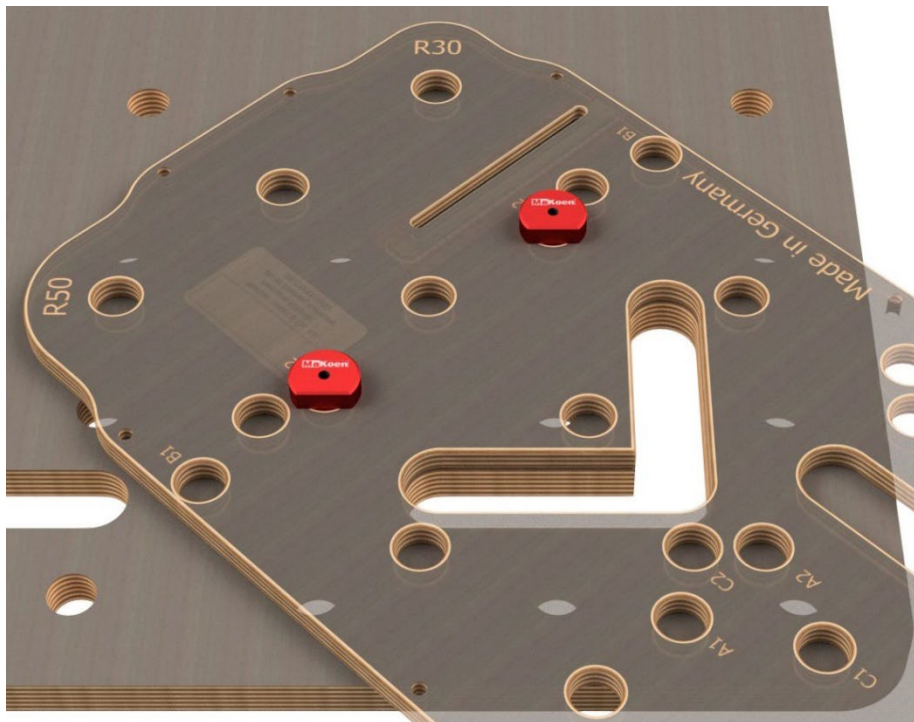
Vinklat långhål genom tillämpning av arrangemang B2
